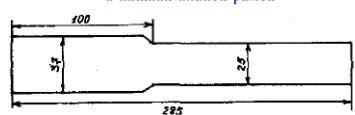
Шаблон для изготовления боковых планок гнездовой рамки
